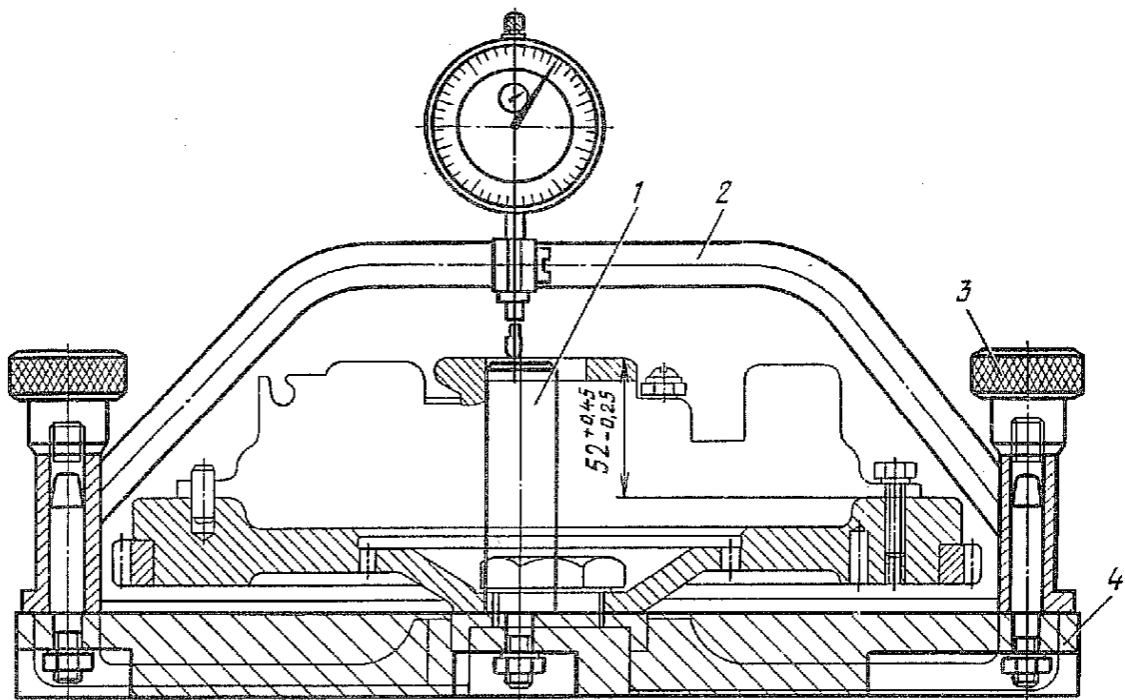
Приспособление для регулировки положения пяты сцепления:
